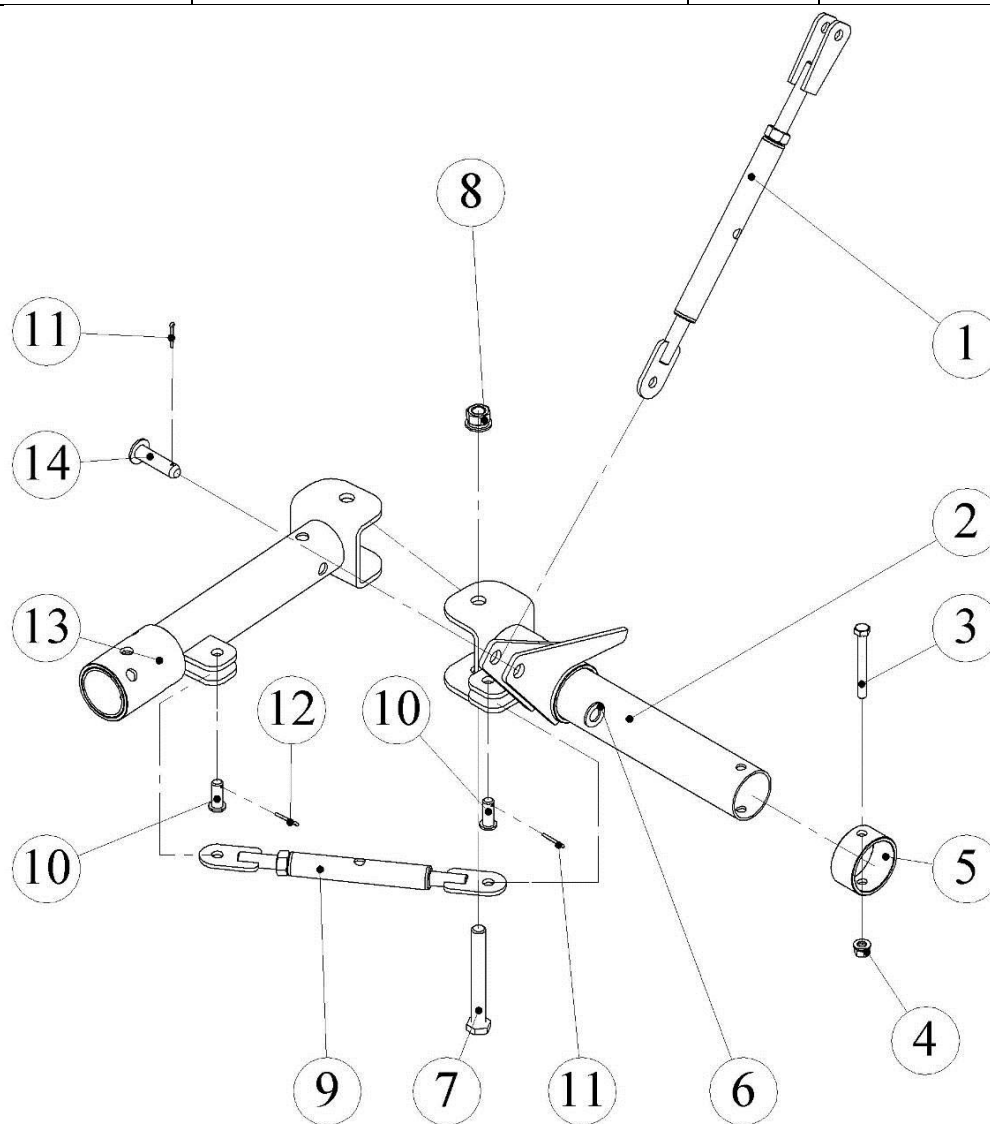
Рычаг поворотный и рычаг подвижный
